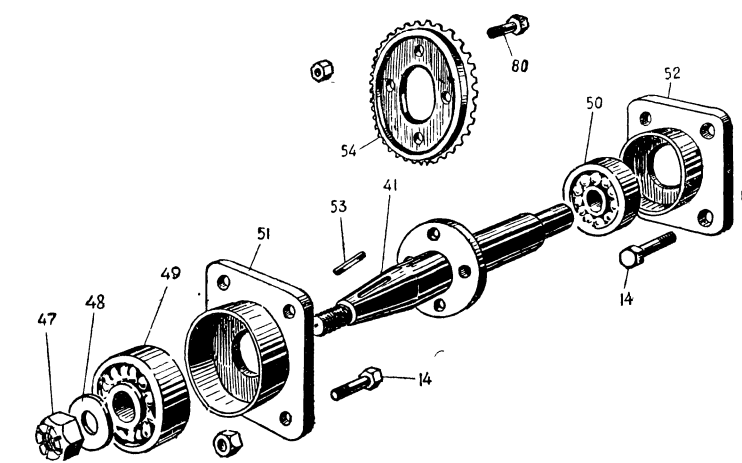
Вал воздушного винта, подшипники с гнездами и ведомая звёздочка.
